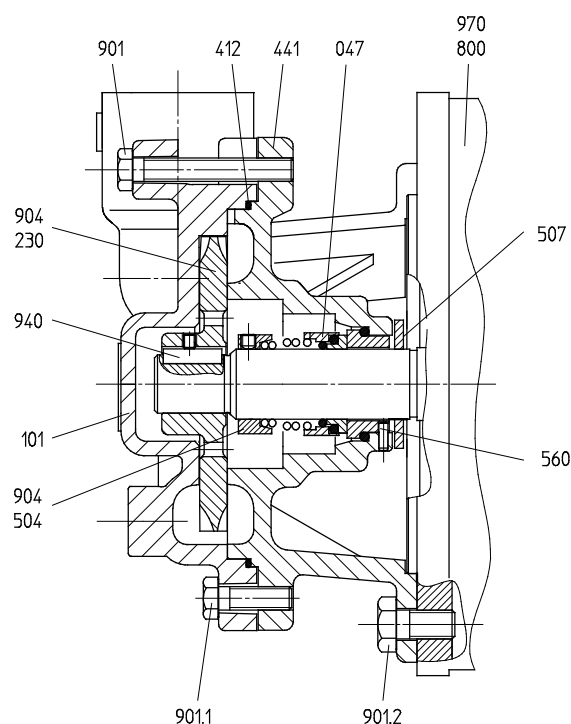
Schnittzeichnung Y-6091 (Edelstahl)
